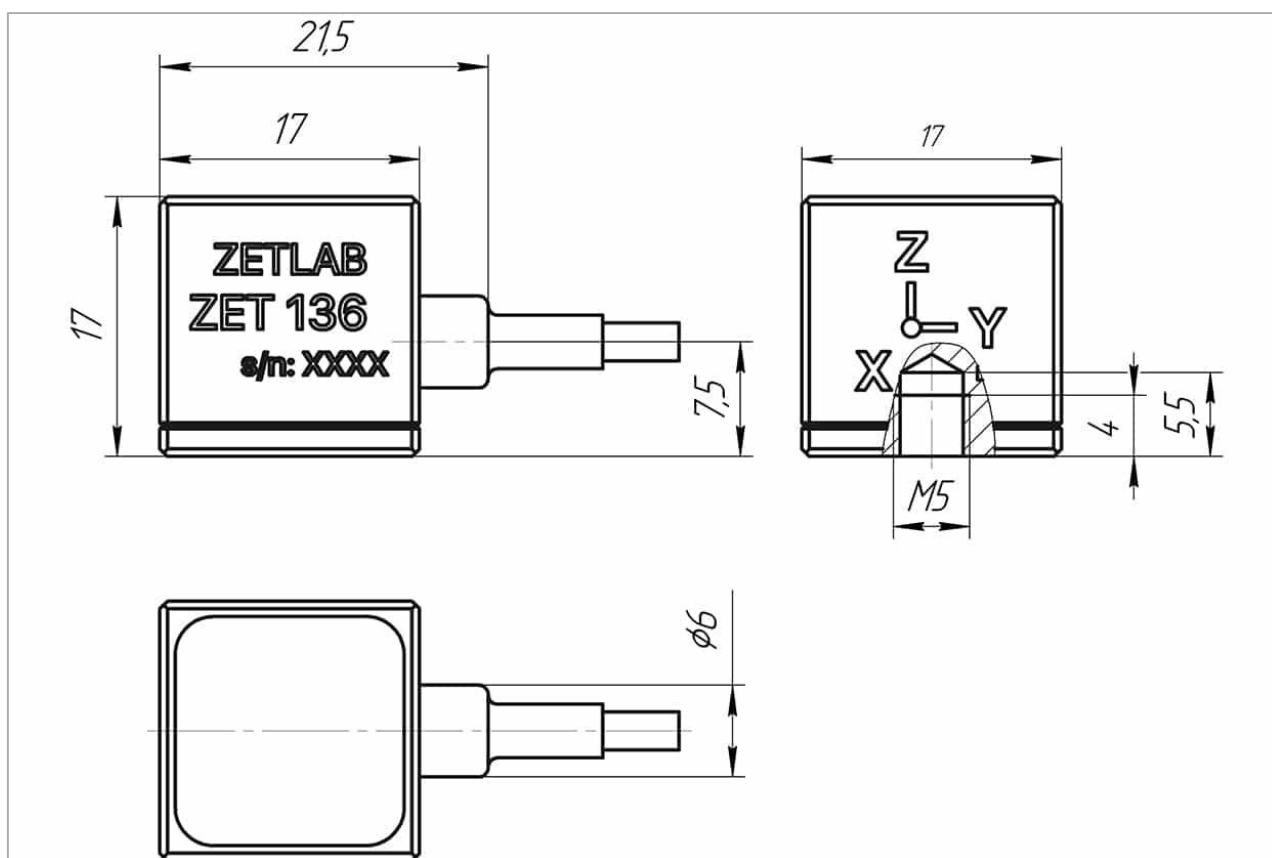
Габаритный чертеж акселерометра ZET 136
